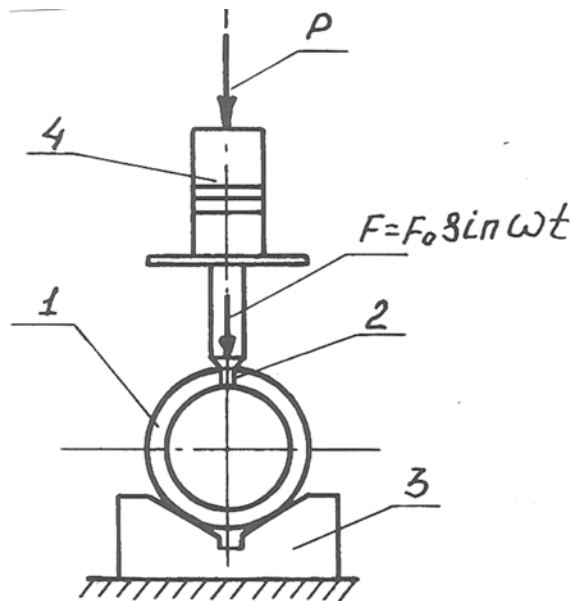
Схема разлома кольцевых деталей: 1 – разламываемая деталь; 2 – концентратор напряжений; 3 – призма; 4 – волновод
